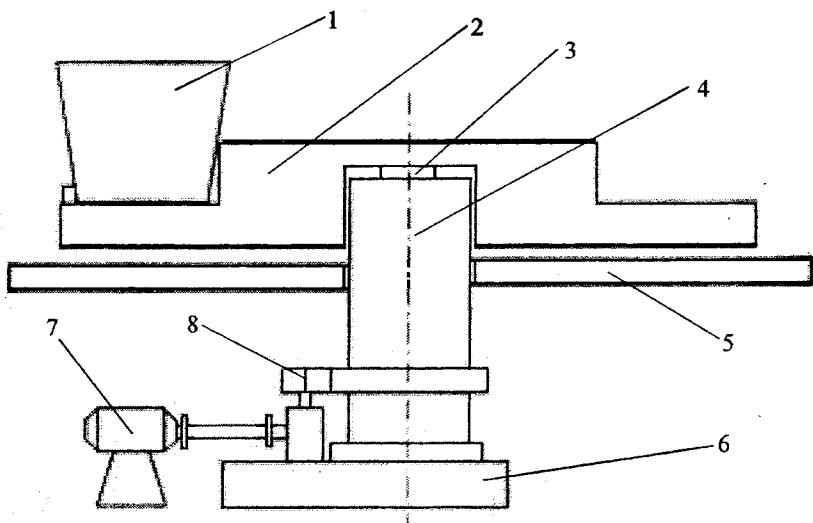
Схема поворотного стола промежуточного ковша:
